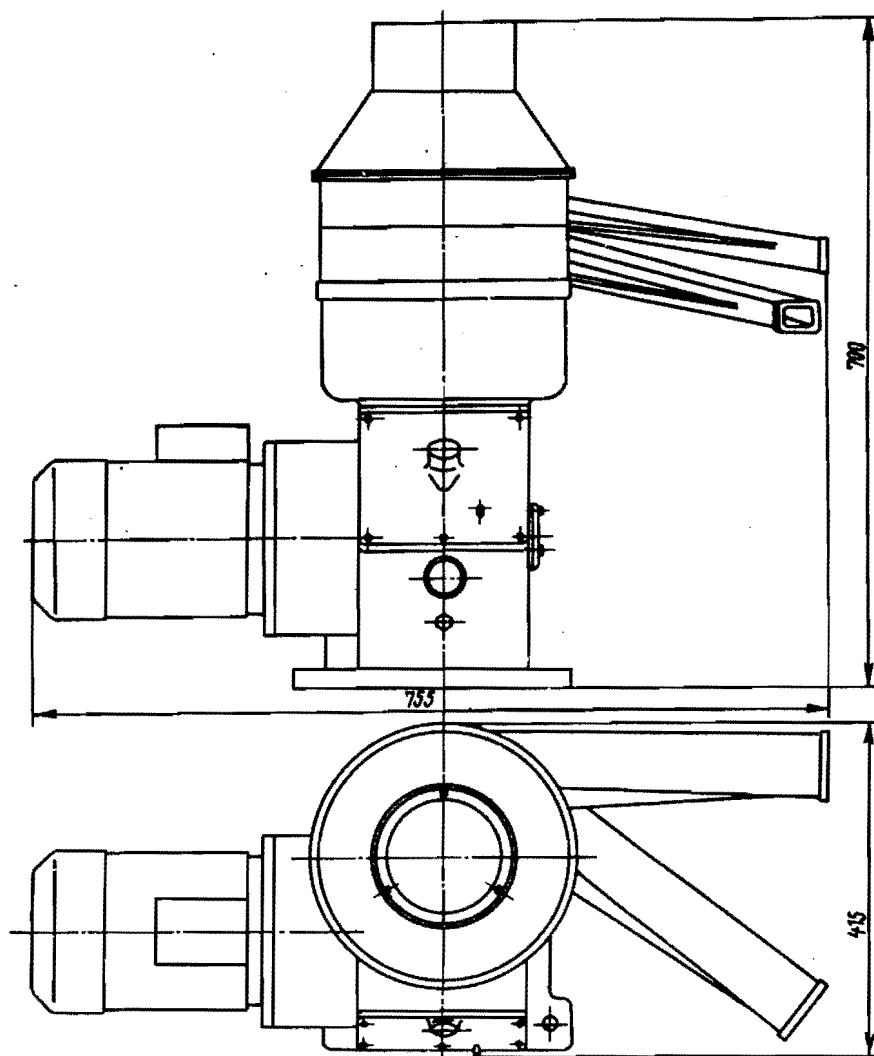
Общий вид сепаратора А1-ОС2-Б
